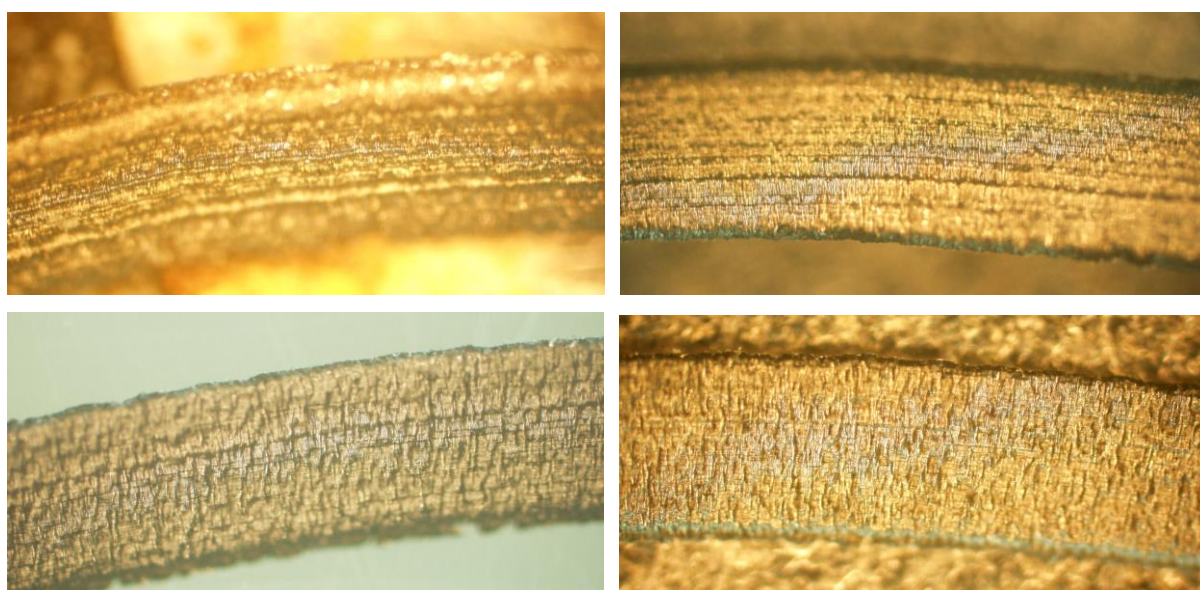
Поверхность стружки при точении образцов 2 (вверху) и 5 (внизу), 100[×].
